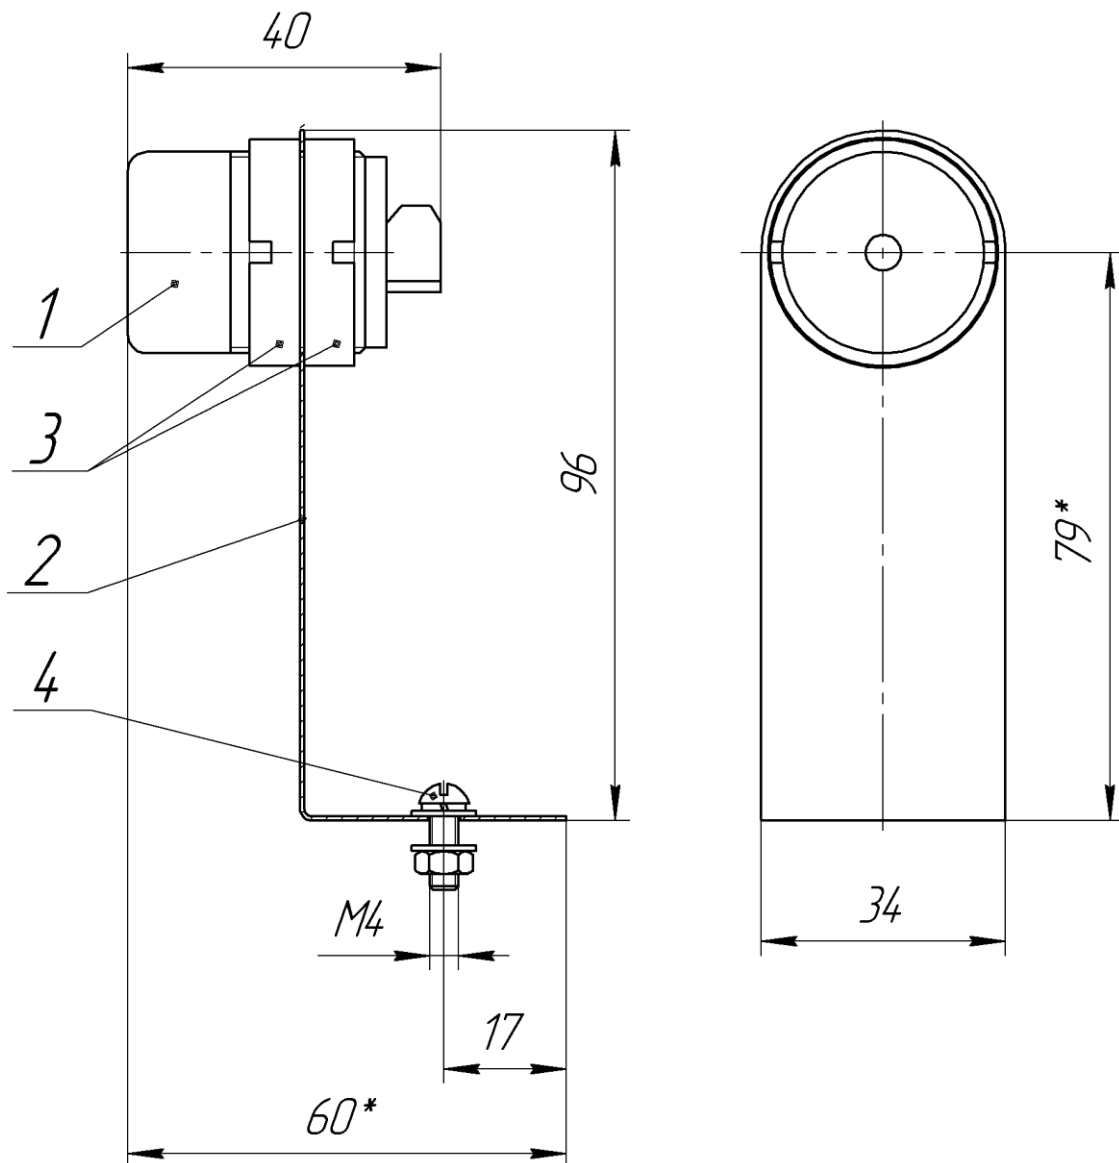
Общий вид, габаритные и посадочные размеры датчика ДДЗ-2Н
